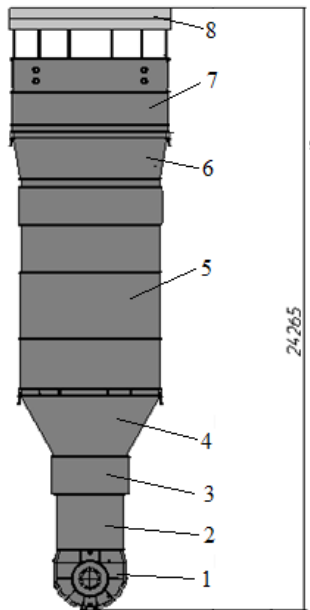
Конструктивная схема новой конструкции выхлопного тракта агрегата типа ГПА-Ц-16С с выравнивателем потока:
